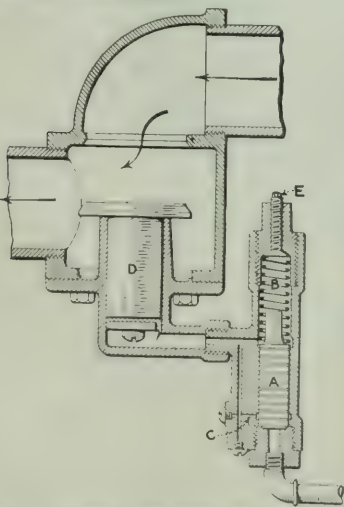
VÁLVULA DE DESCARGA PARA EL TUBO ASPIRANTE
